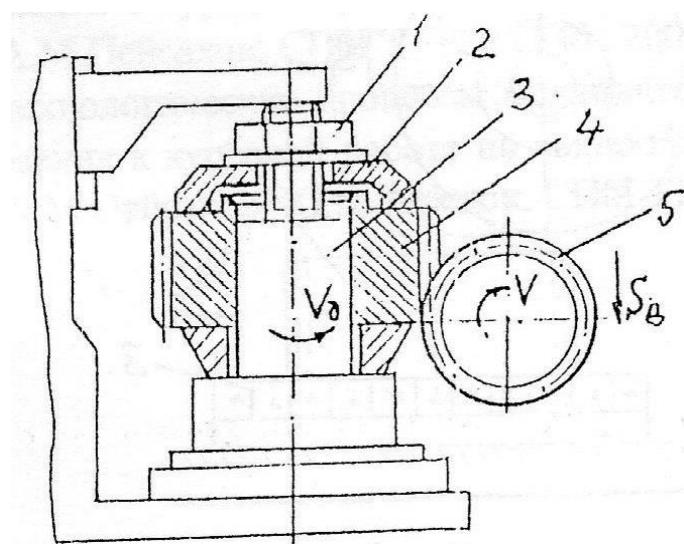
Схема обработки зубчатого колеса на 050 и 055-й операциях:
